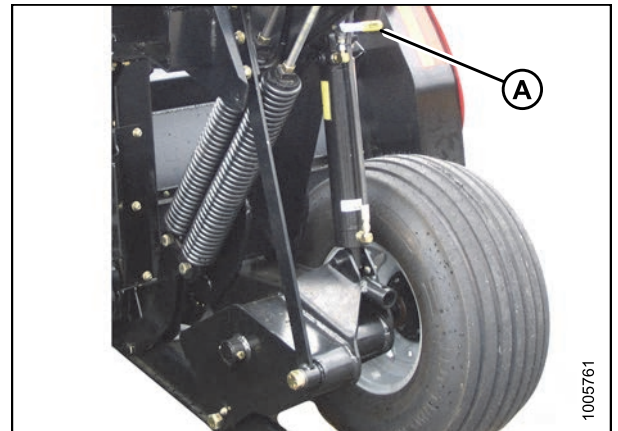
Рукоять клапана блокировки цилиндра
